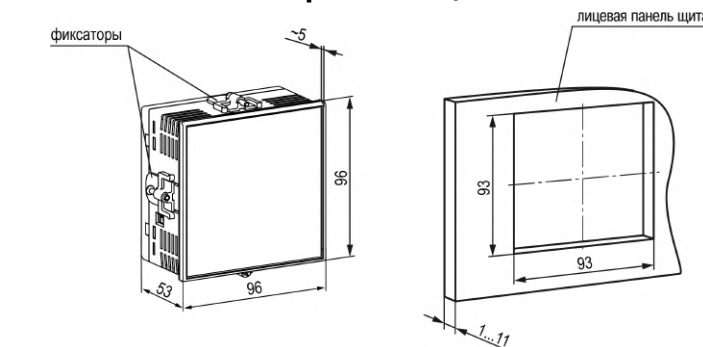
Габаритные размеры корпуса Щ1 и монтажного отверстия в щите
